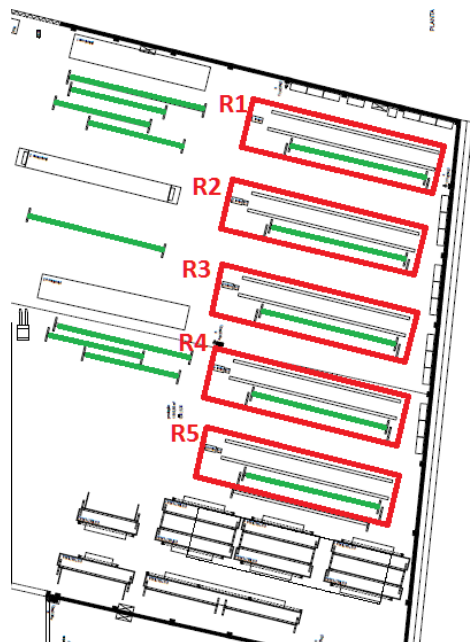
FPT: Ficha de Planeamento de Tela; Planta Produção Robots
